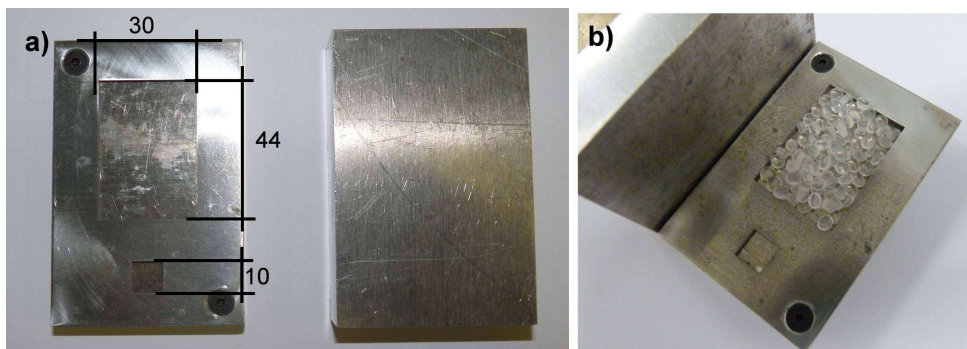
Moule utilisé pour réaliser les plaques de LLDPE à partir des granulés (a), dépôt des granulés dans le moule (b) [dimensions en mm].
